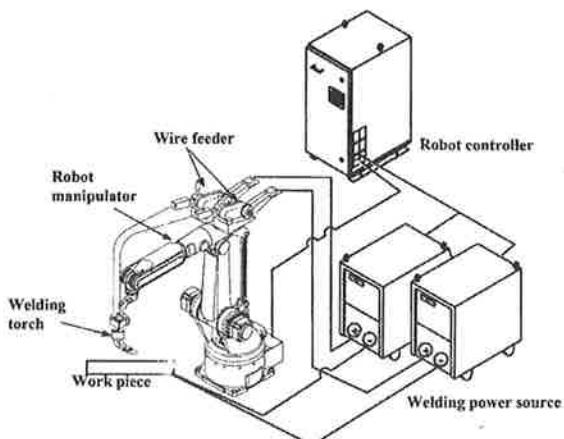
ロボットタンデム(多電極)アーク溶接装置の外観
